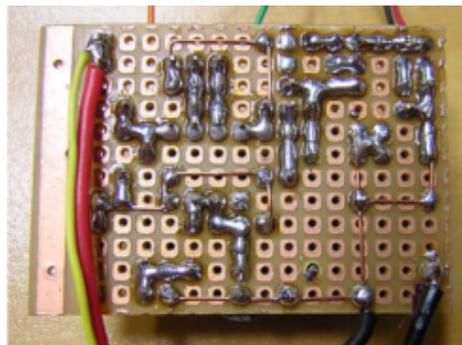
Placa universal com ilhas soldadas fazendo a conexão entre terminais.
